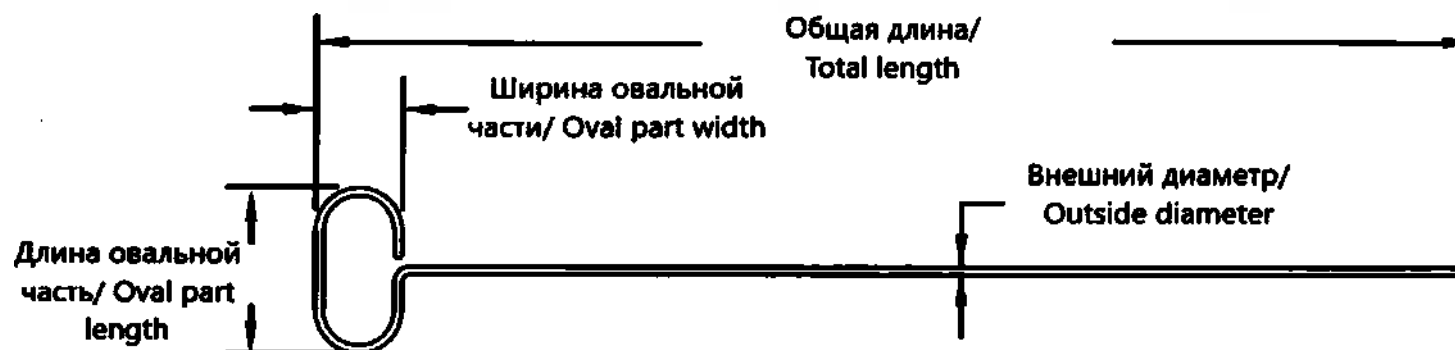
Формирующий мандрен / Picture 6 Shape Mandrel
